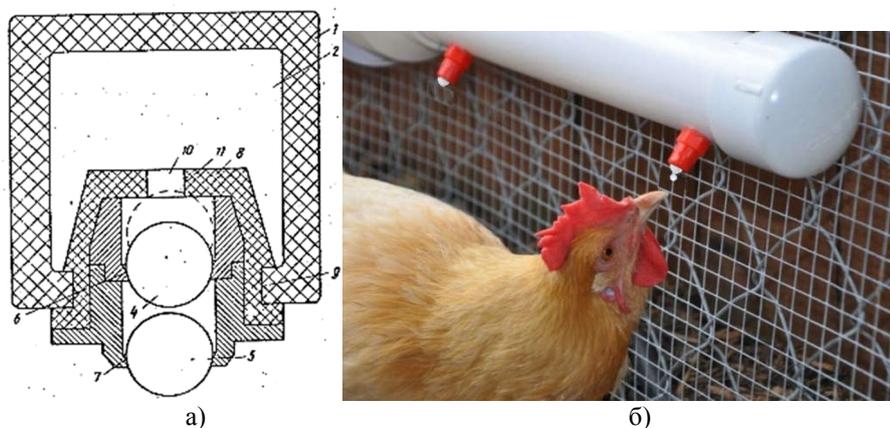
Схема (а) и общий вид (б) поилки для птиц с двухклапанной системой шарикового типа
